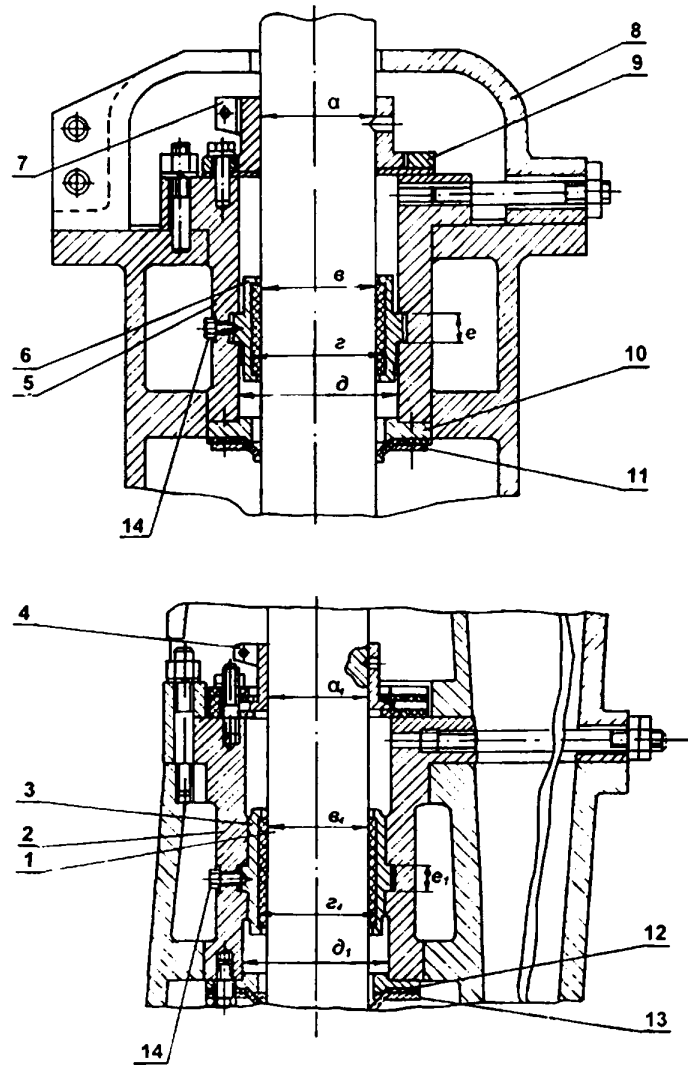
Корпус сальника (рис. 7, 10, поз. 16)
